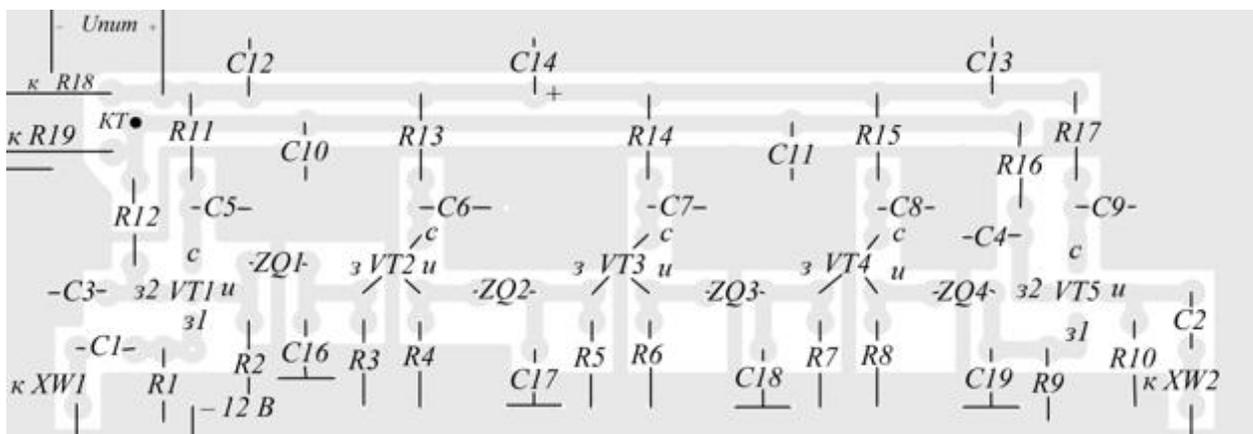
Эскиз монтажной платы УПЧ с кварцевыми резонаторами (активным кварцевым фильтром). КТ – контрольная точка. Вид со стороны установки деталей
